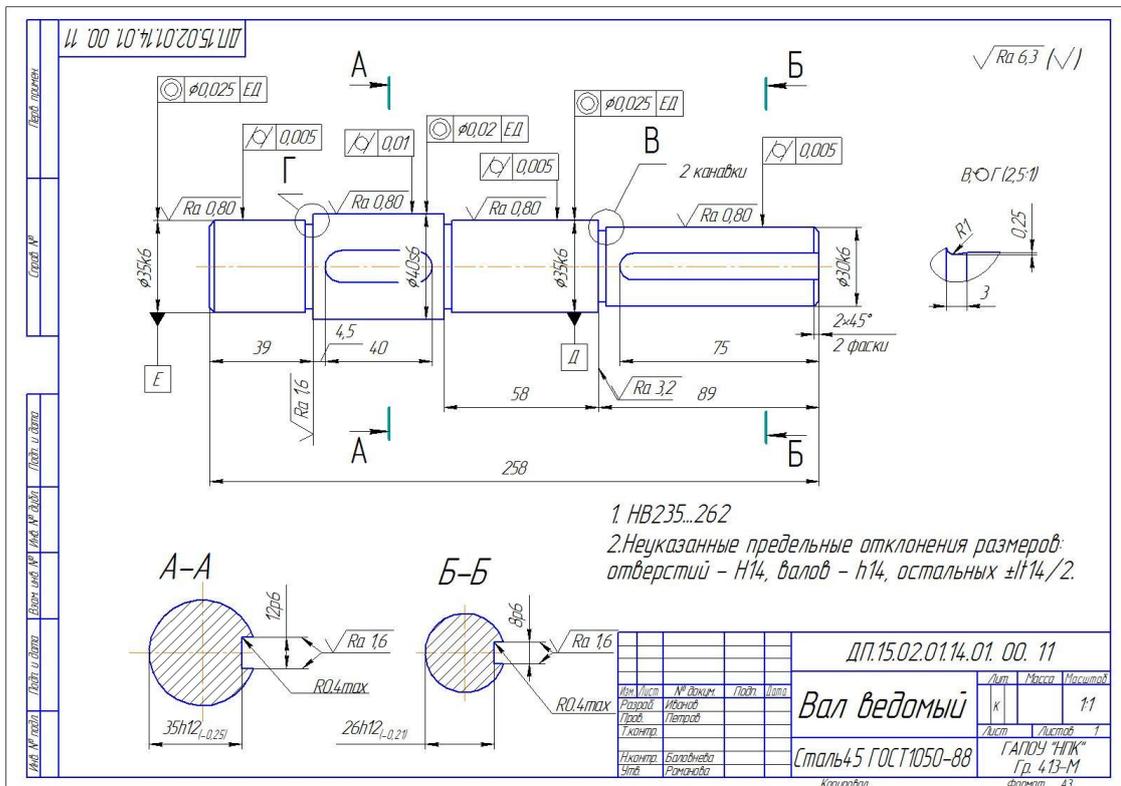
Пример выполнения чертежа детали «Вал ведомый»
